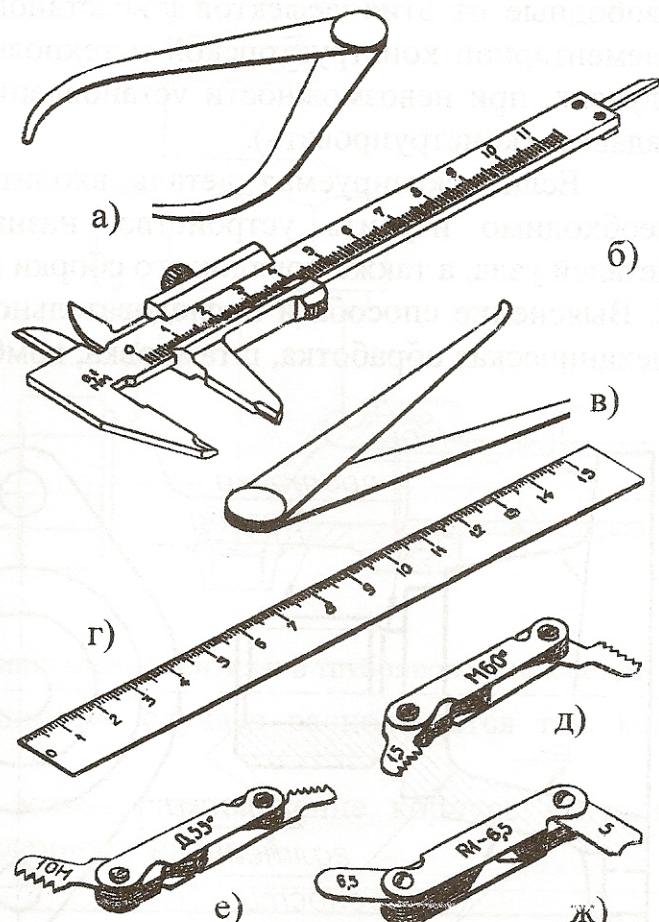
Инструменты, применяемые при эскизировании: а – кронциркуль; б – штангенциркуль; в – нутромер; г – масштабная линейка; д – резьбомер для метрических резьб; е – резьбомер для дюймовых резьб; ж – радиусомер
